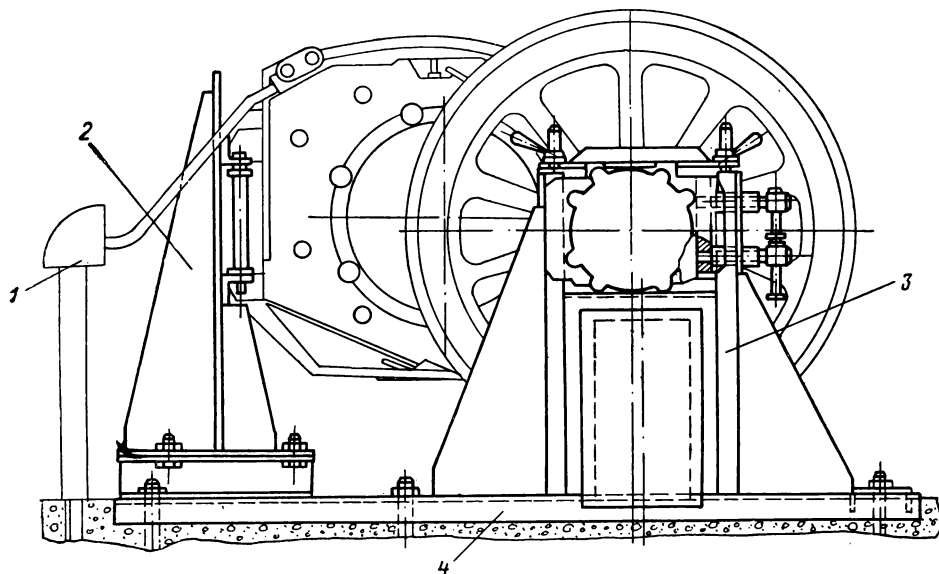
Стенд для сборки и обкатки колесно-моторных блоков:
